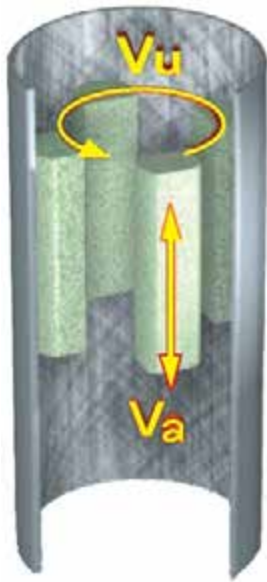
ro-58: Движение хона при обработке цилиндрической поверхности; источник: Atlantic GmbH
